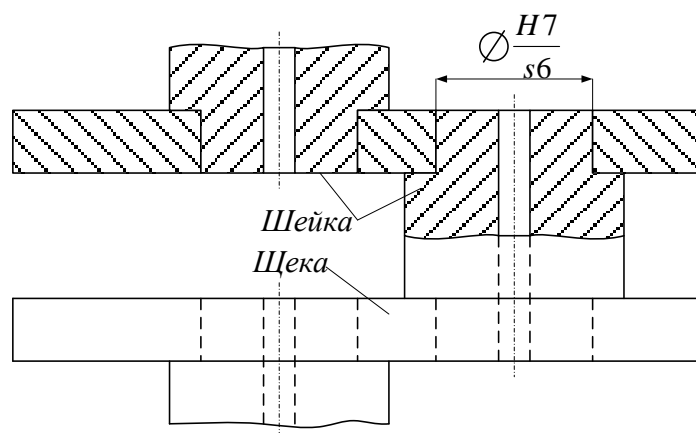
Применение прессовых посадок при изготовлении коленчатых валов
